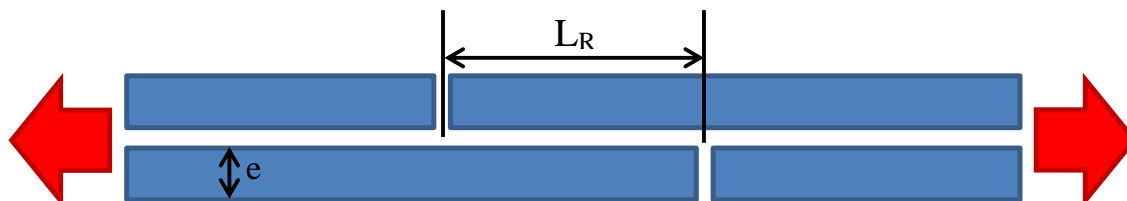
Architecture d'une plaque avec joint à simple recouvrement (2 couches = 4 plis)
